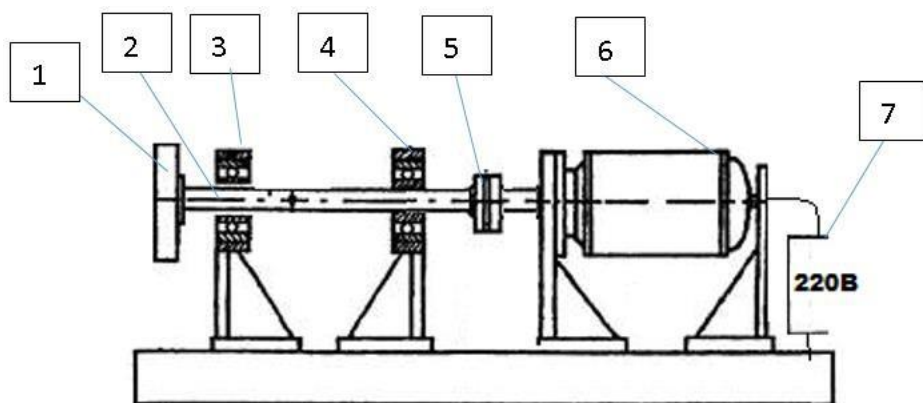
Схема механизма роторного типа с двумя опорами и рабочим колесом
